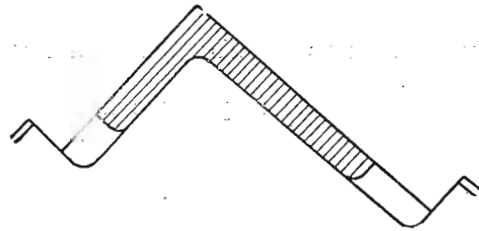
Чистовой калибр для прокатки угловых профилей с разной шириной полки
